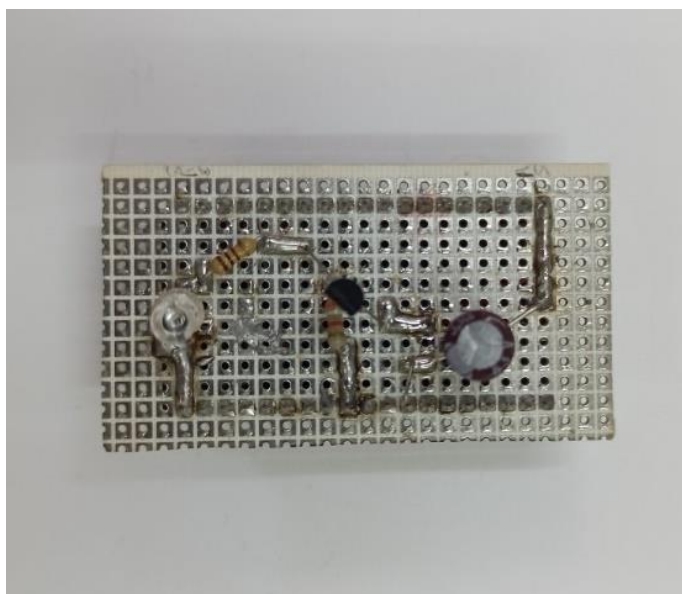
Montaje real del módulo IR por la cara de los componentes.
